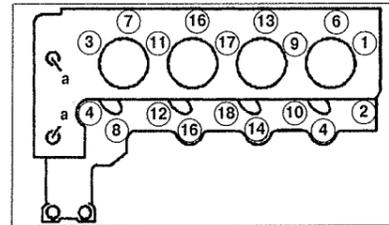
Порядок ослабления болтов крепления головки блока цилиндров
